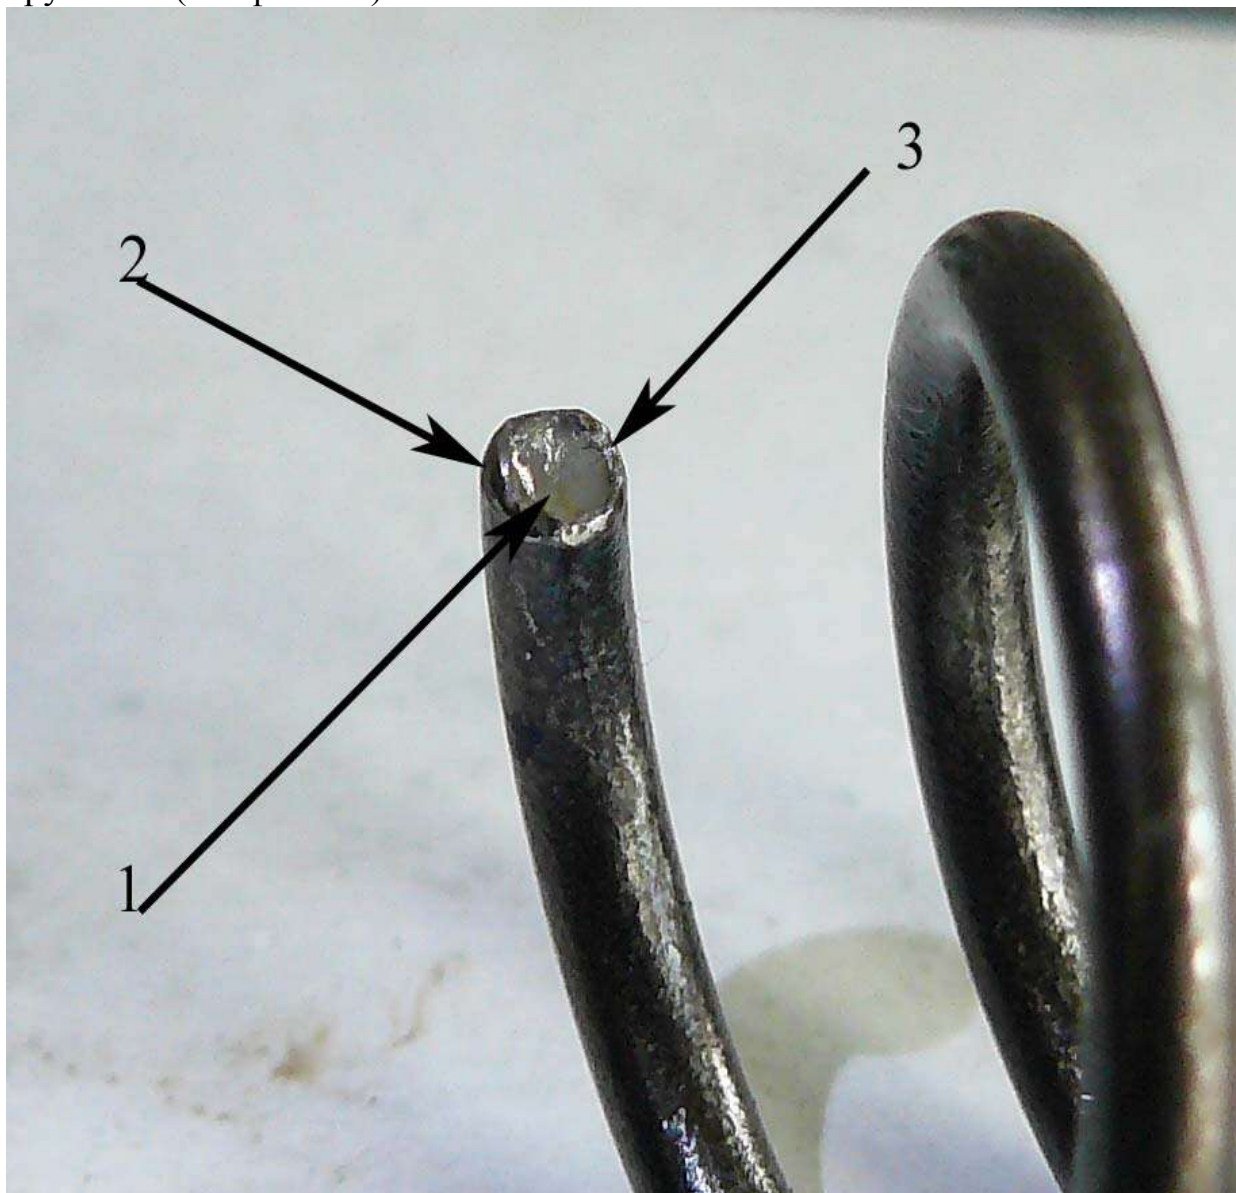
Поверхность излома внутренней пружины: 1 — излом; 2 — зона окончательного разрушения; 3 — зона образования усталостных трещин
